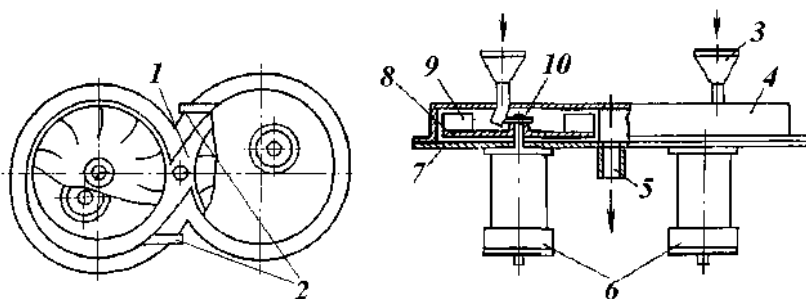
Принципиальная конструкция центробежной противоточной мельницы: 1 – тангенциальный канал; 2 – разгрузочный патрубок; 3 – загрузочный патрубок; 4 – корпус; 5 – выгрузочный патрубок; 6 – электродвигатель; 7 – плита; 8 – диск ротора; 9 – разгонная лопатка; 10 – вал.
